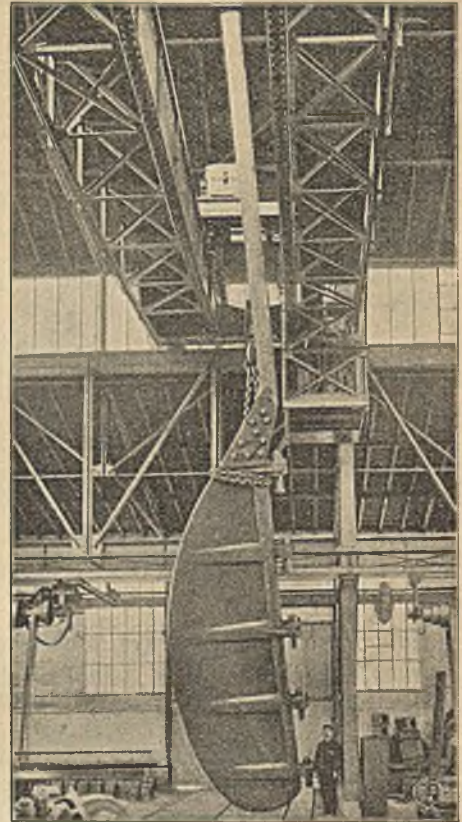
Ruder mit gegossenem Blatt für einen Doppelschraubendampfer, 12 000 kg. (Stahlwerk Krieger.)
